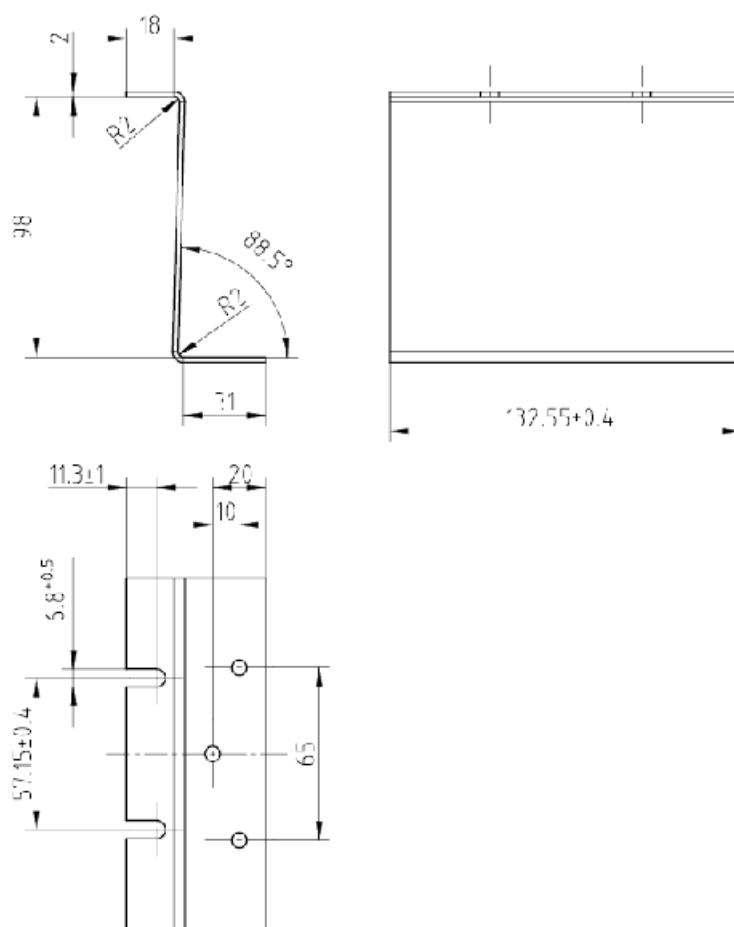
Support de montage pièce latérale X-300EEC (cotes en mm)
